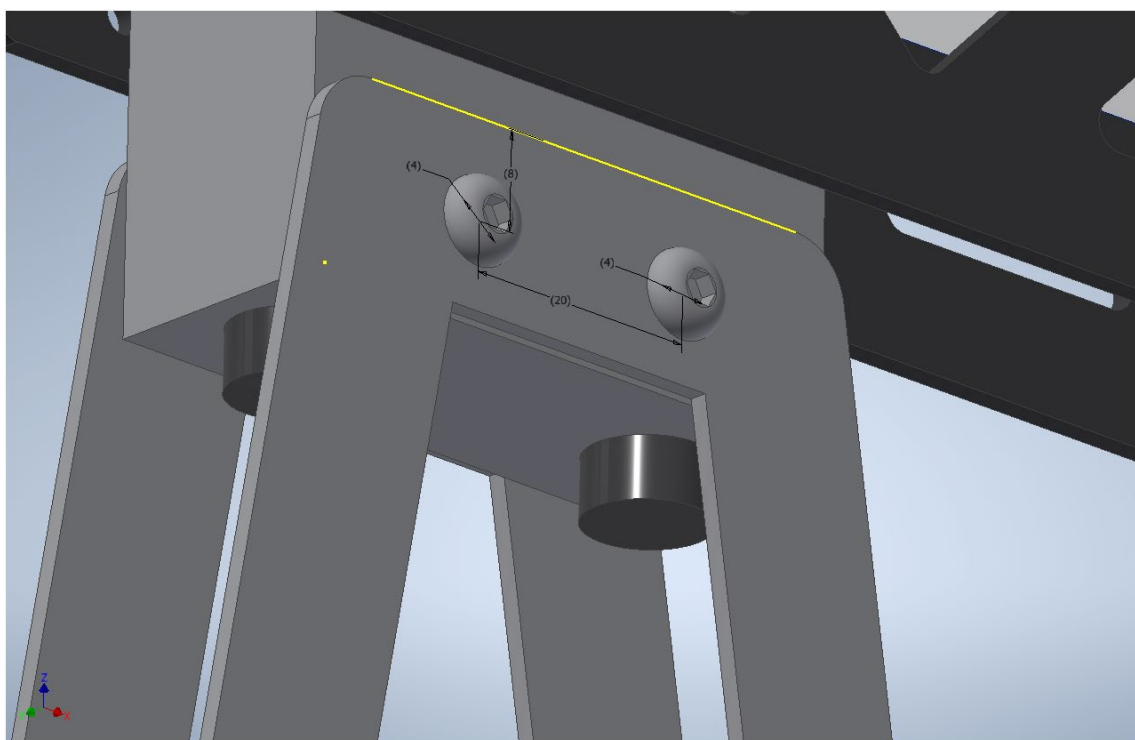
Схема закрепления пластин к рейке крепления полезной нагрузки.
